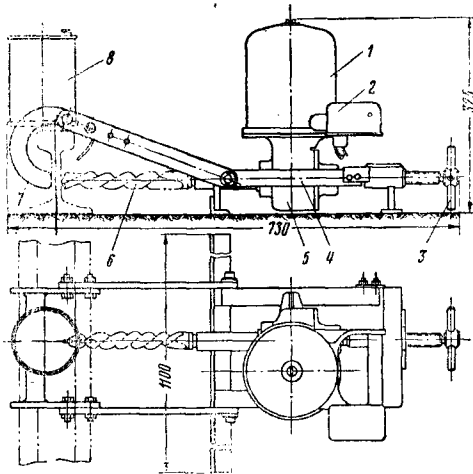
Общий вид электросверлилки ДТ-23-У на станке для сверления рельсов
